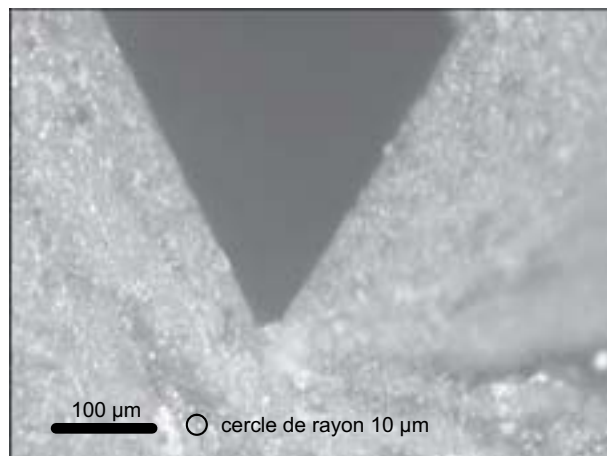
Photo de l’empreinte de l’arête de coupe : plaquette revêtue - TiN.
